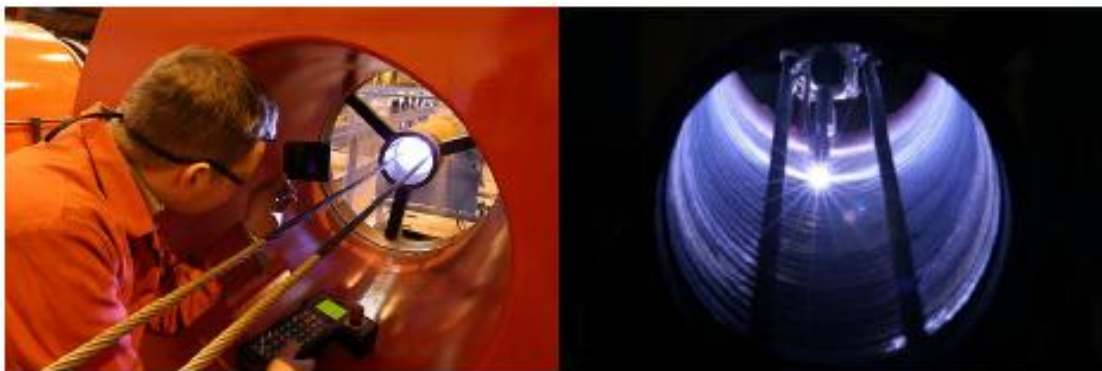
Revestimento interno de tubos utilizando o TIG automático (IODS - Weld Cladding, Pipe Cladding, Clad Pipe Fittings and Fabrication, 2014)
